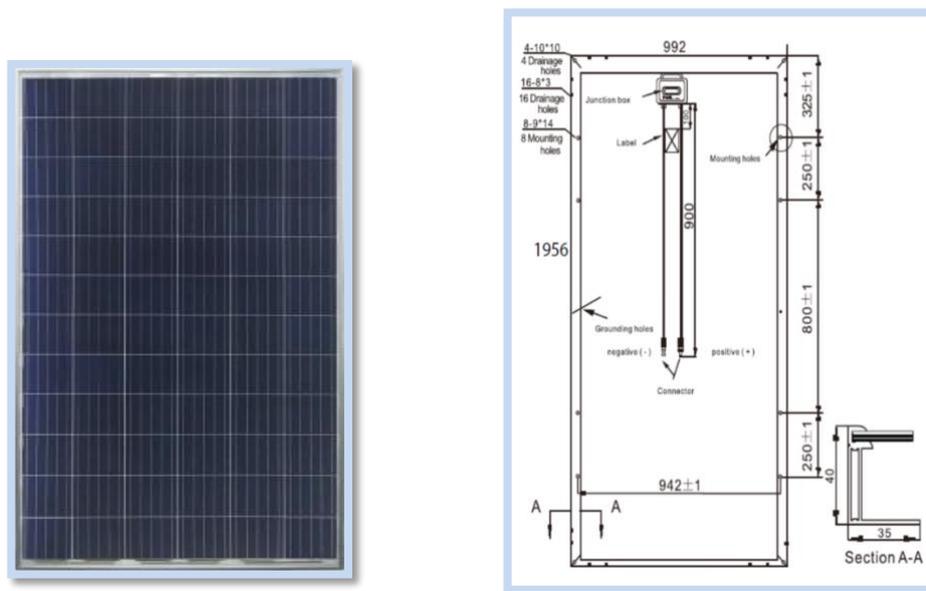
Dimensions du panneau pour le modèle N6P305W-320W.
